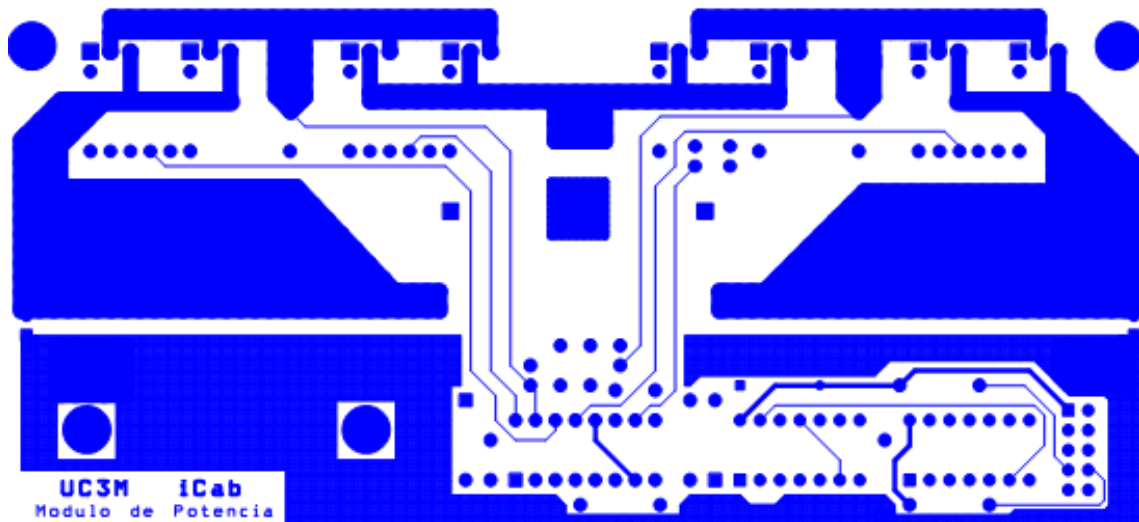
Placa del módulo de potencia Layout final. Capa TOP
